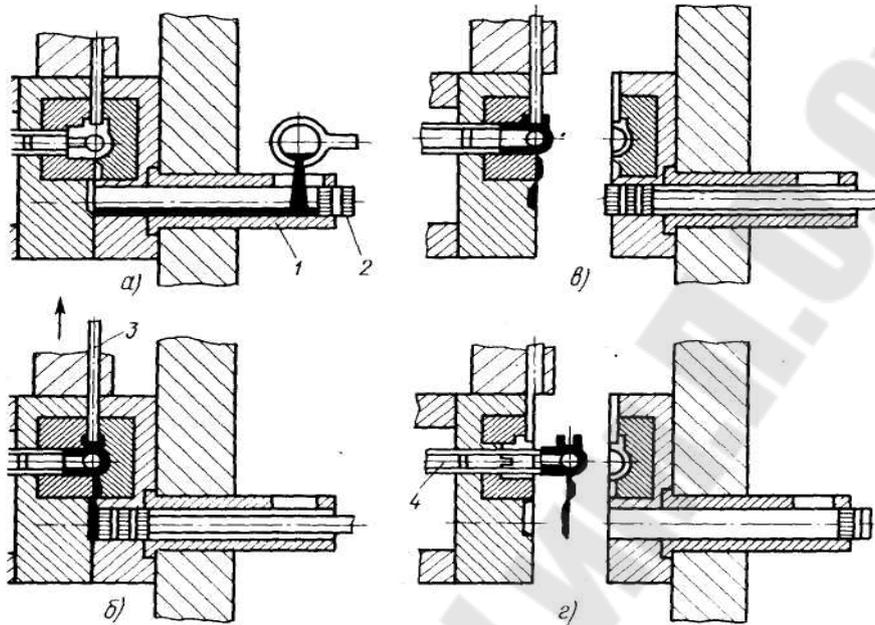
Схема процесса литья под давлением: а- заливка, б- запрессовка, в- разъем пресс-формы, г- выталкивание отливки; 1- камера прессования, 2- поршень, 3 - стержень, 4- выталкиватель
